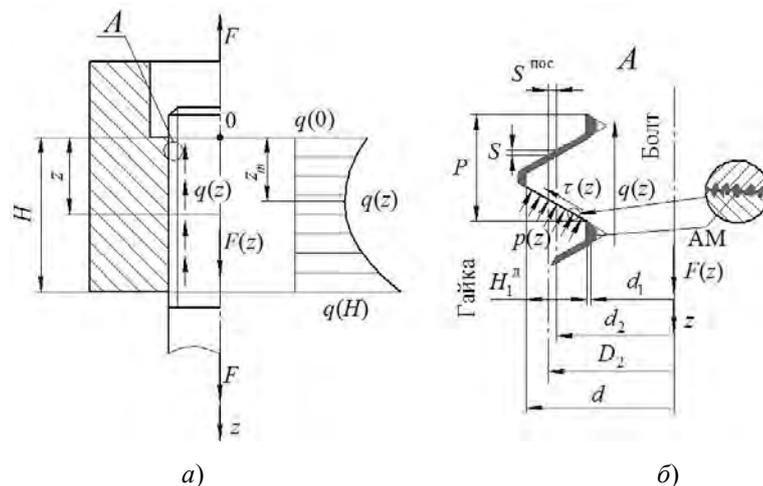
Схема нагружения резьбового соединения типа стяжки:
